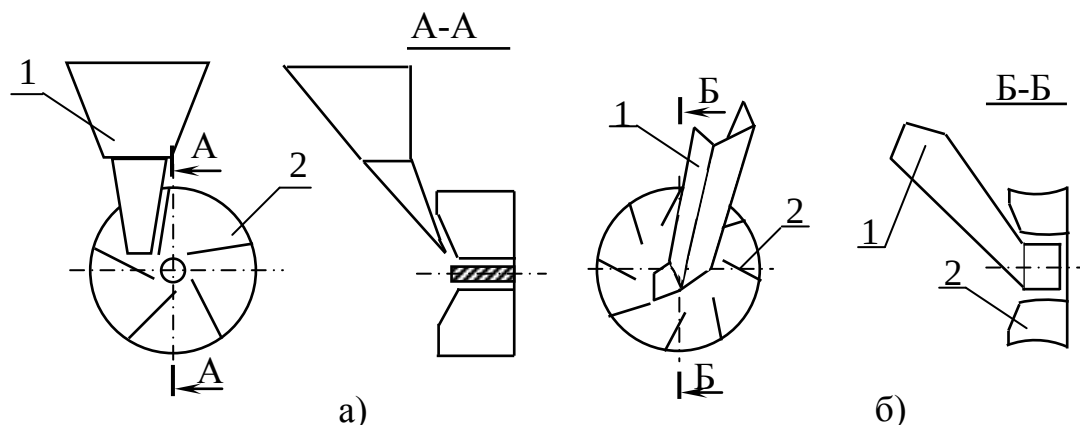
Схемы способов подачи зернового вороха на лопатки диска метателя
